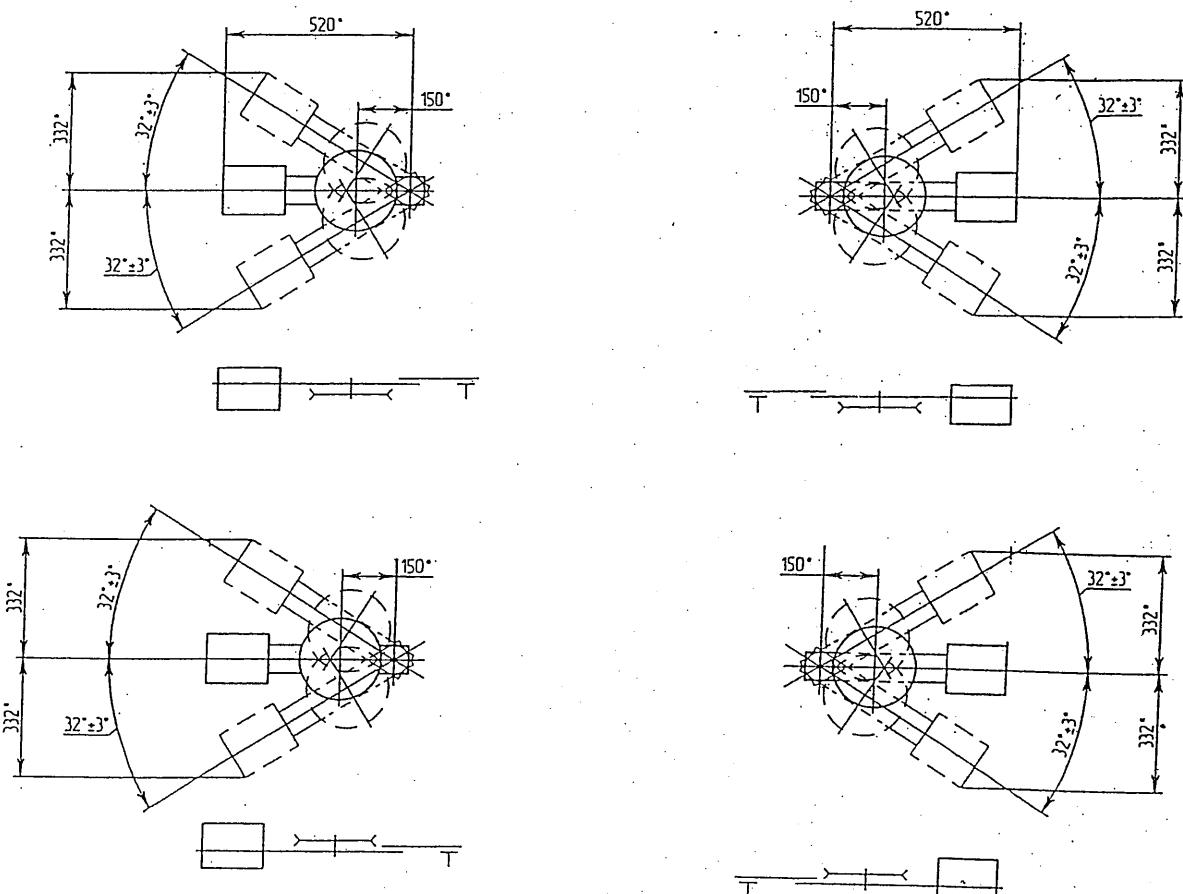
схемы сборок натяжного устройства каната ОС
